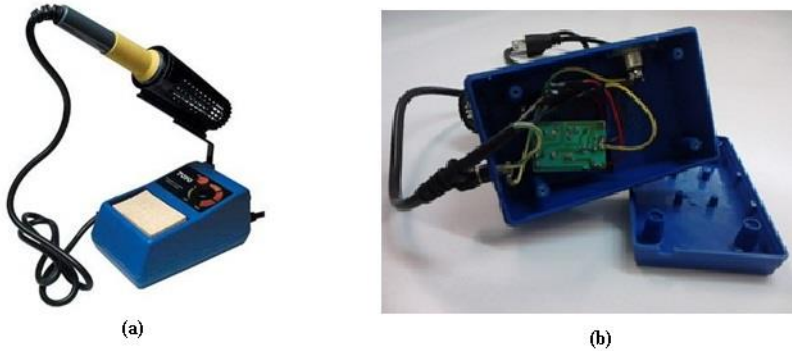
Estação de Solda – TS – 900 (a); Configuração original de fábrica (b).
